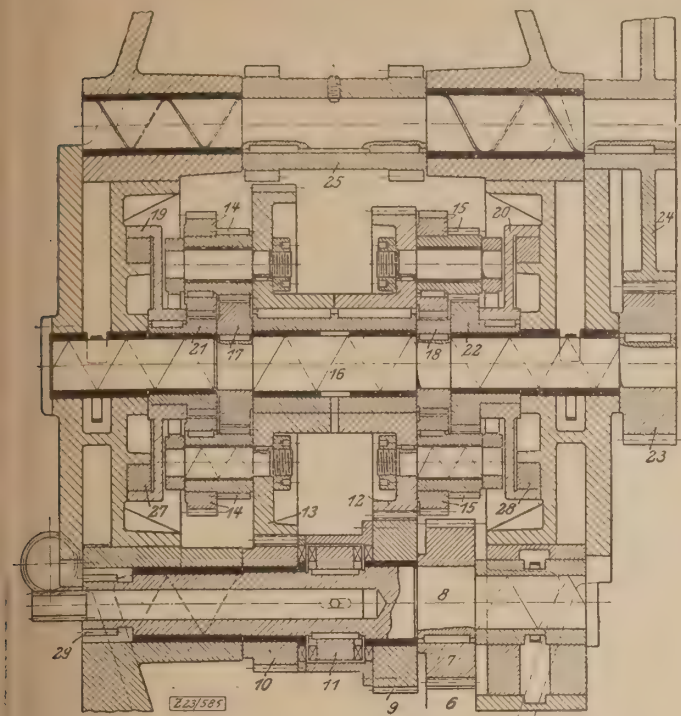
Planetenschaltwerk zur Stoßmaschine von Lange & Geilen. Hauptantrieb der Maschine möglich
